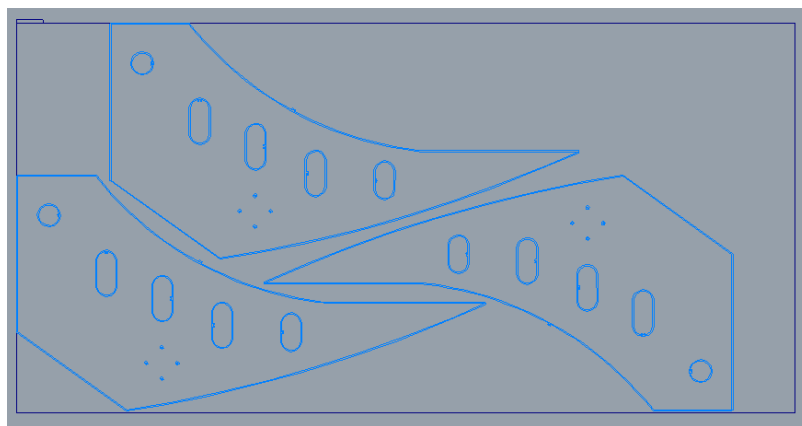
Positionnement des pièces sur la deuxième tôle.
